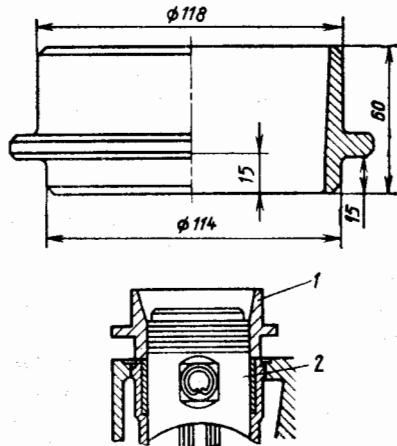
Приспособление для установки поршней в сборке с шатунами в цилиндр
